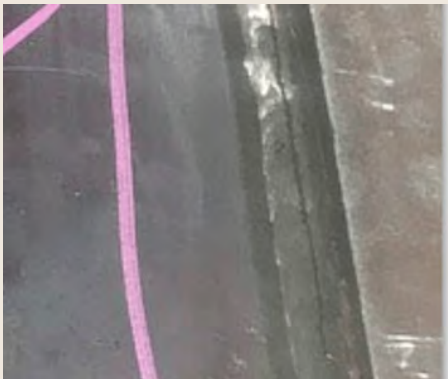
g Soldadura agrietada longitudinalmente.
